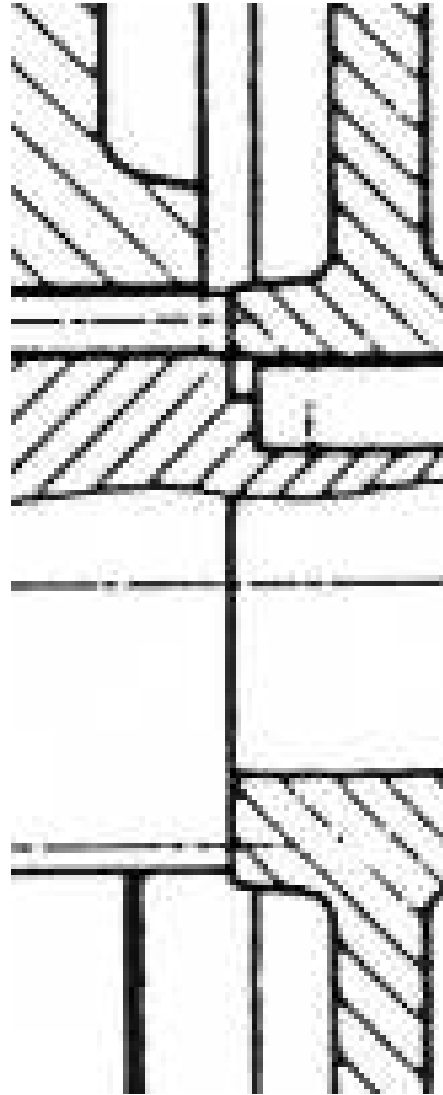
Zoom sur la section épaulée (échelle 1 : 1).
